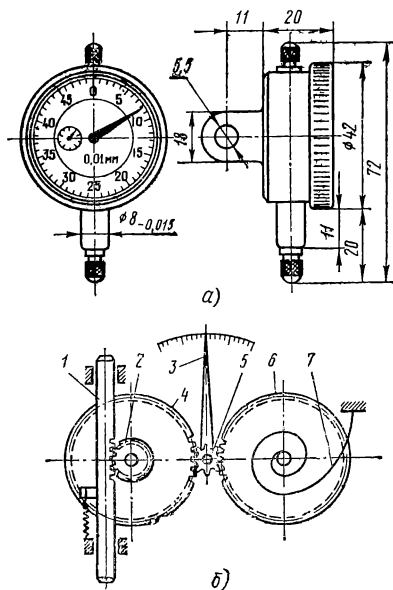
Малогабаритный индикатор (а), схема зубчатой передачи (б)
